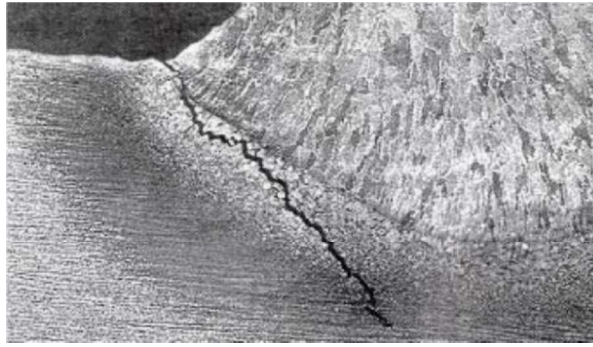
8 - Fissura em união soldada (Toptitech, 2024).
